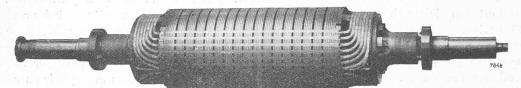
Rotor d'un turbo-alternateur, 3000 t/m.
